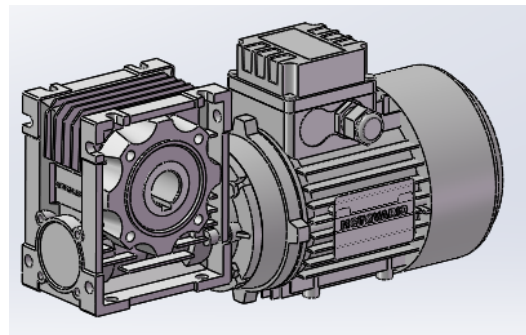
Motorreductor Motovario con reductora de tornillo sinfín.
